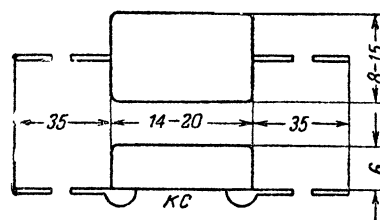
Габаритный чертеж стеклоэмалевых конденсаторов.
